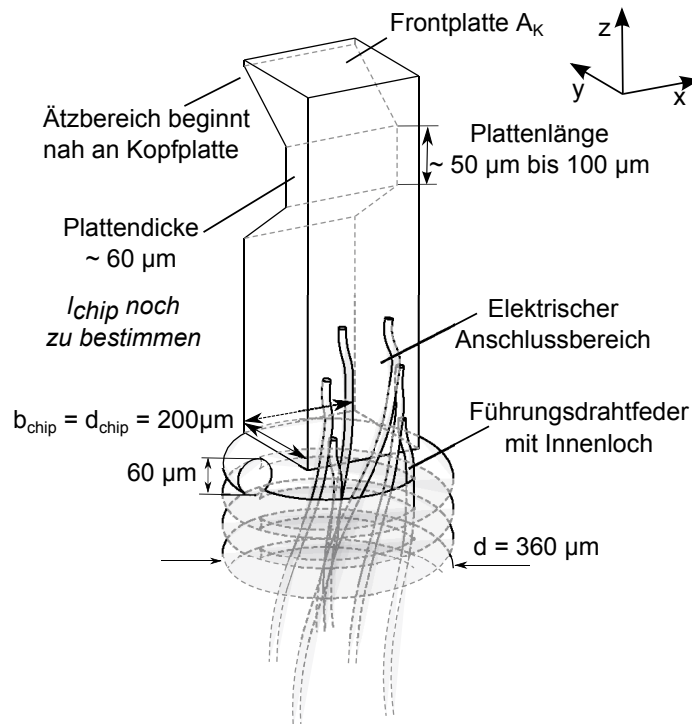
In die Führungsdrahtspitze integriertes Messelement, mechanischer Teil.
